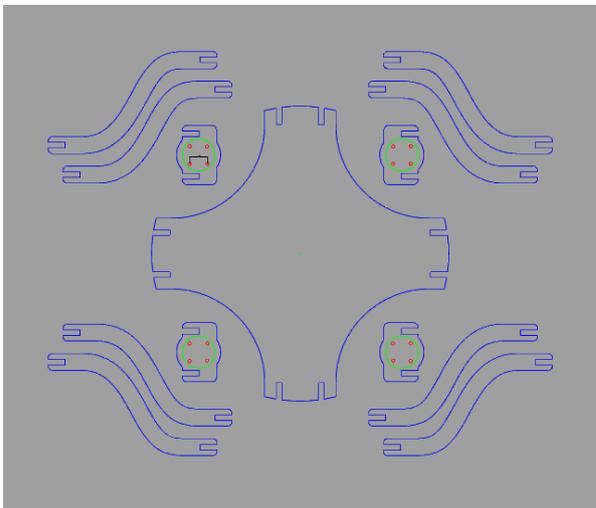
Desenvolvimento de 2º *mock-up* em software 3D para usinagem em CNC
